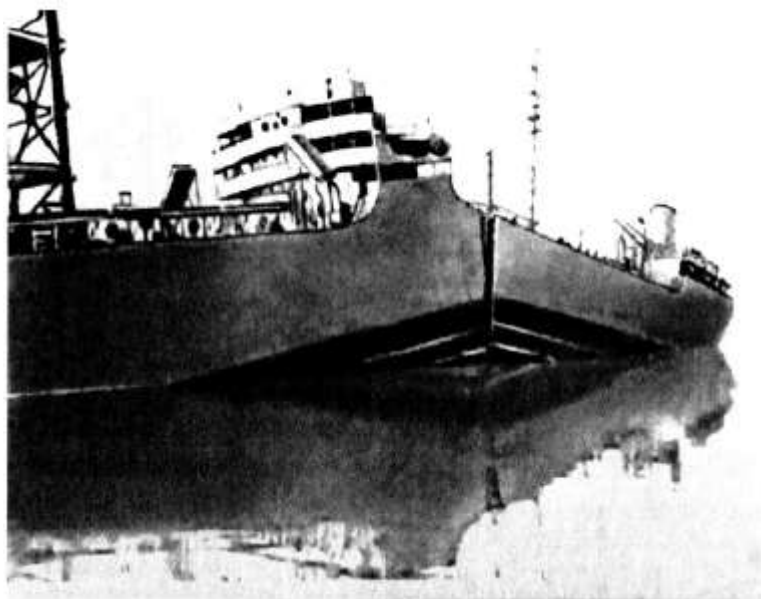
Хрупкое разрушение сварного танкера
